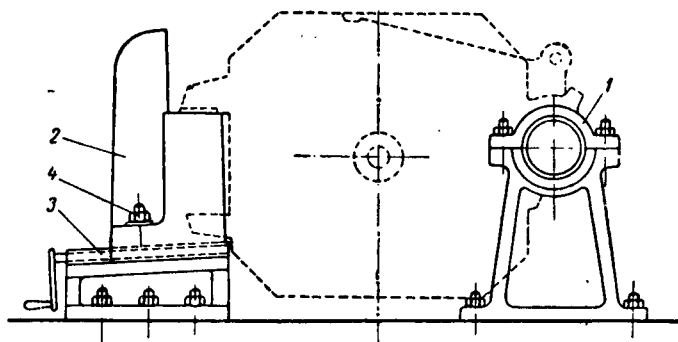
Опоры для установки тяговых двигателей на стенде:
